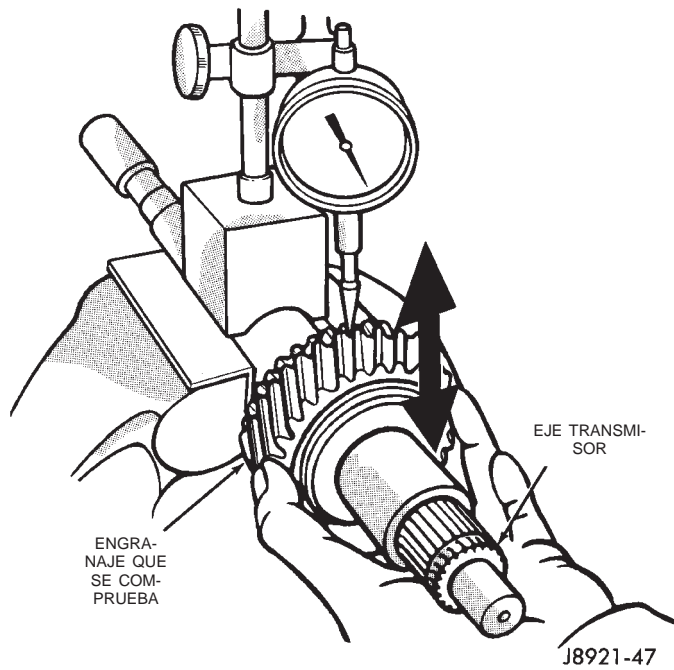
Comprobación de holgura de lubricación entre engranajes y eje
